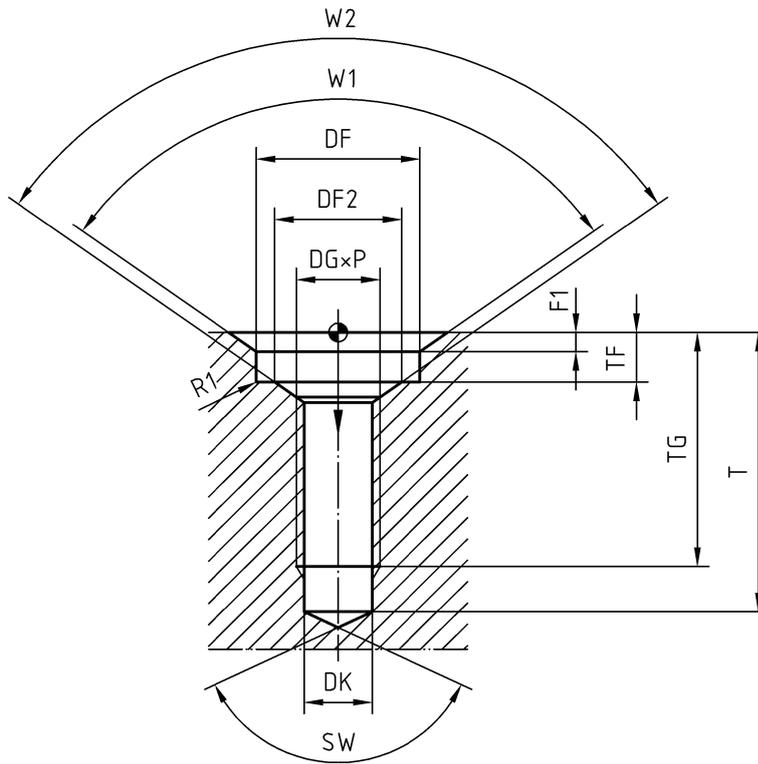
Gewindegrundbohrung mit Flachsenkung
